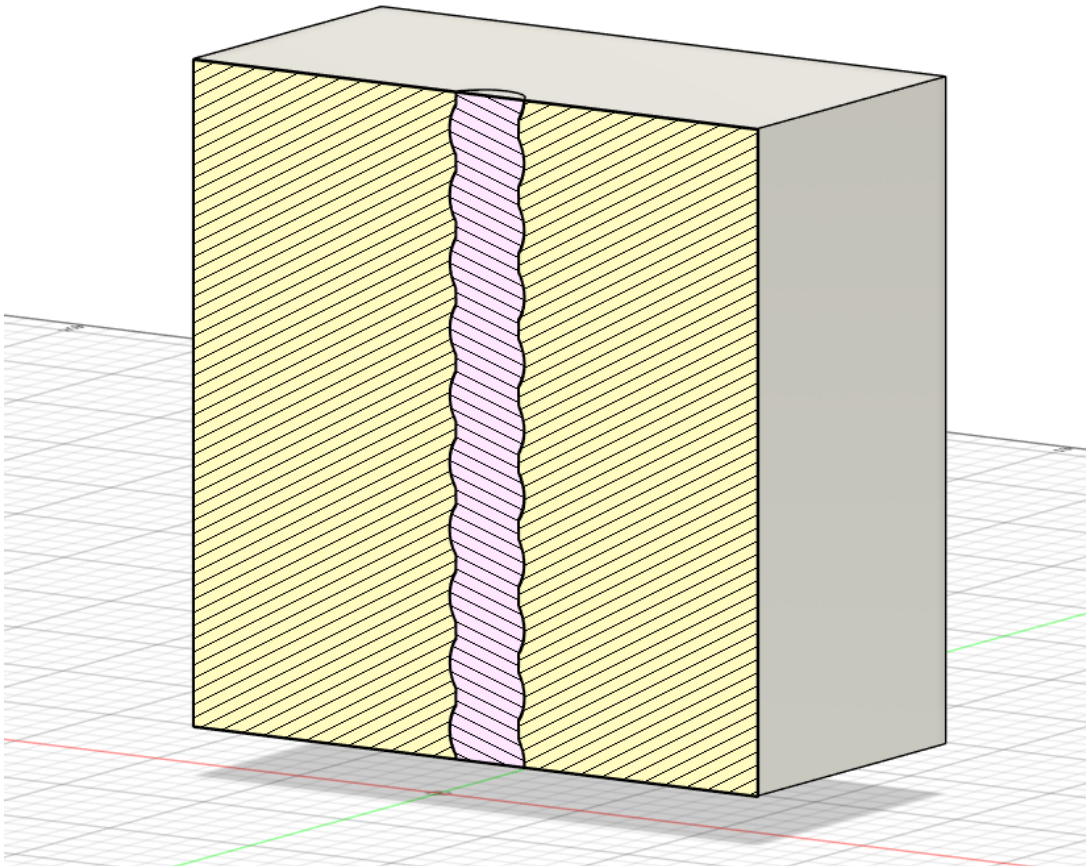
Початкова 3D-модель для розрахунків
